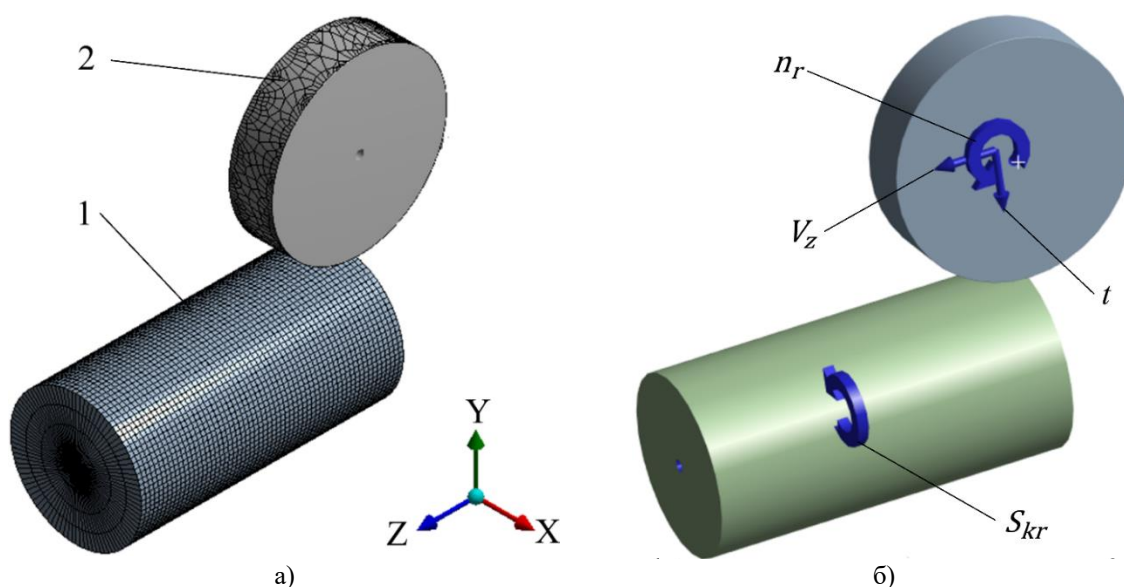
Конечно-элементная модель процесса строчного ППД (на примере базового цилиндрического ролика – вариант I): а – дискретизация расчетной области (гексаэдральная сетка на заготовке); б – кинематика инструмента: 1 – заготовка; 2 – деформирующий инструмент (ролик)
